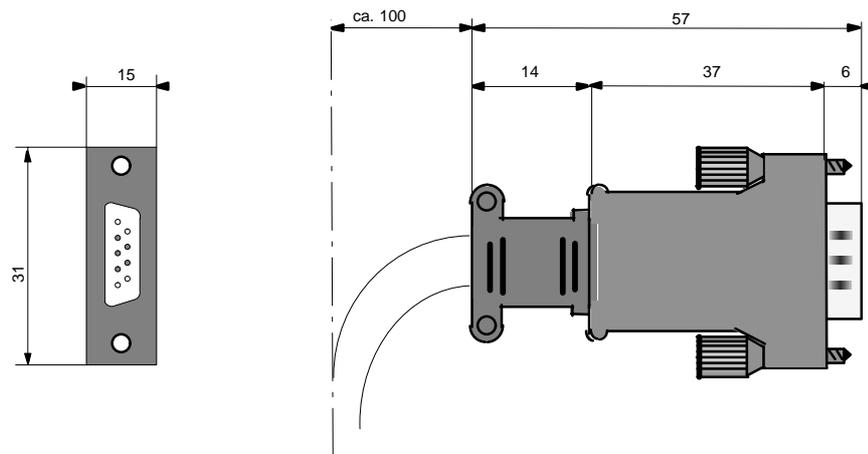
9-poliger Sub-D-Stecker für Selbstmontage (Maße in mm)
